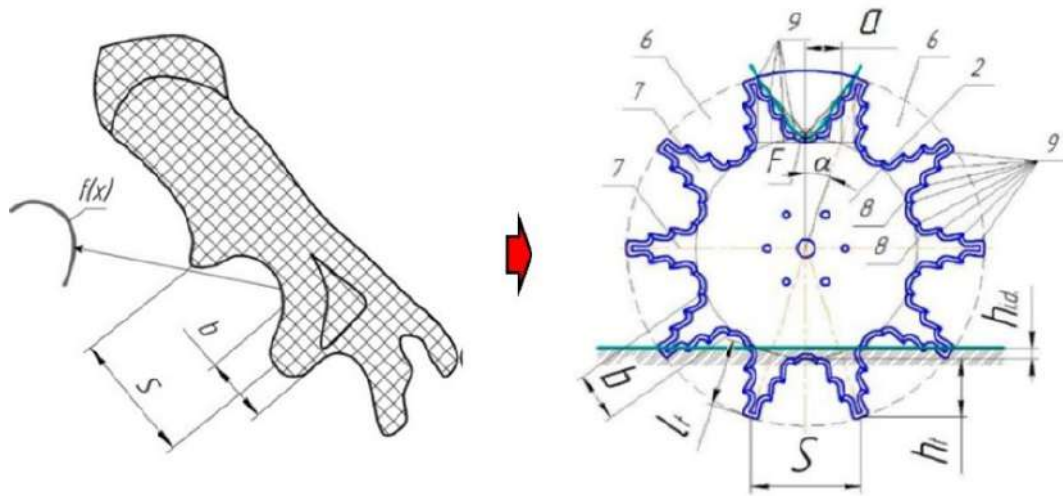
Конструкція робочих органів культиватора на основі поворотних дисків із зубами на основі кінцівки жука-носорога
